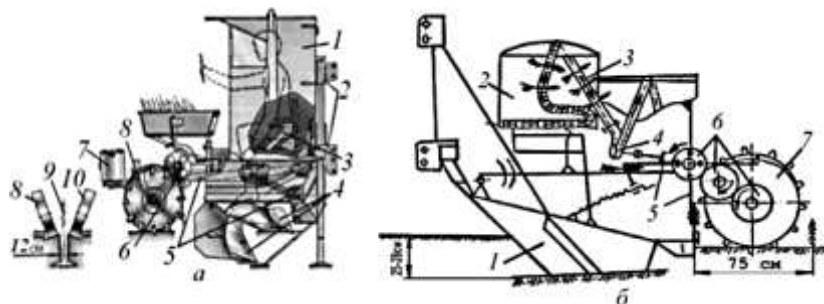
Общее устройство лесопосадочной машины с ручной подачей семян (а): 1 – кабина; 2 – рама с навеской; 3 – сиденье; 4 – сошник; 5 – подвижная рамка с подвеской; 6 – посадочный аппарат; 7 – балластный ящик; 8 – прикатывающе-приводной каток; 9 – сеянец в почве; 10 – прикатывающий каток;
